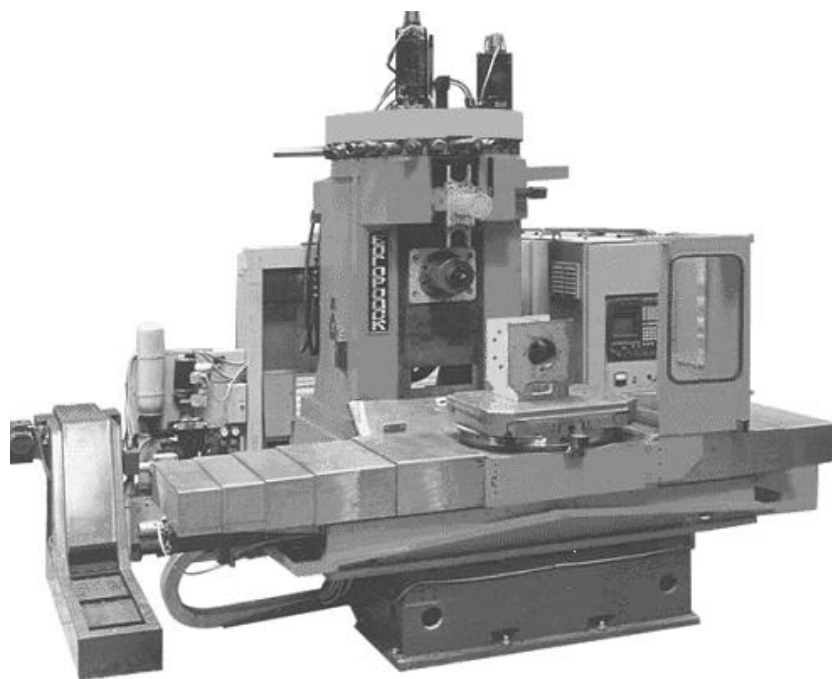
Обрабатывающий центр мод. IP800PM8Ф4 для комплексной обработки корпусных деталей (сверление, зенкование, развертывание, растачивание отверстий по координатам, обработка деталей с поворотом стола, фрезерование плоскостей и пазов сложной конфигурации).
